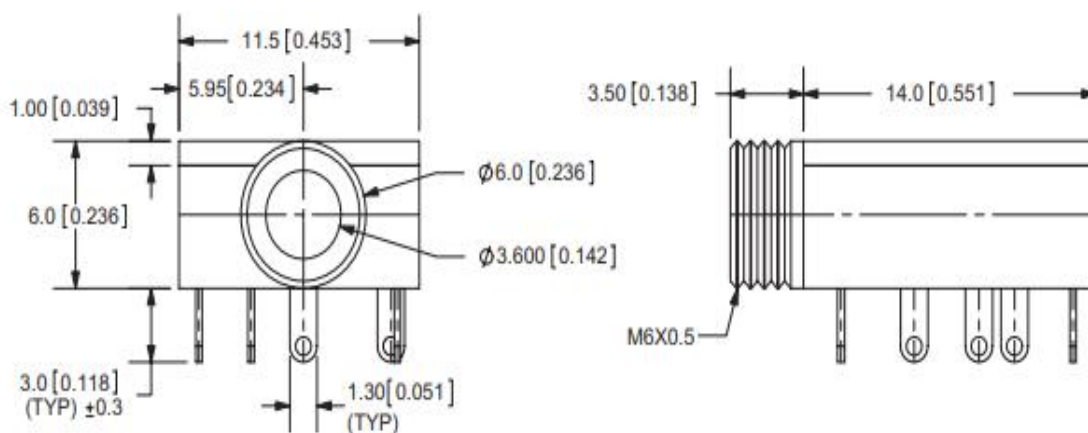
Габаритні розміри роз'єму SJ1-3513
